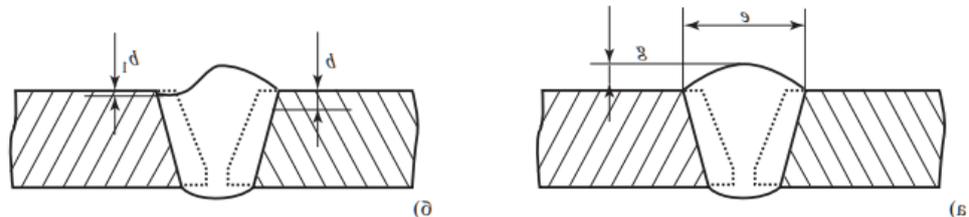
Размеры кольцевого шва сварного соединения, подлежащие измерительному контролю: а) размеры шва сварного соединения: е – ширина; g – высота; б) дефекты шва сварного соединения: b – глубина несплавления, выходящего на поверхность; b1 – глубина подреза
